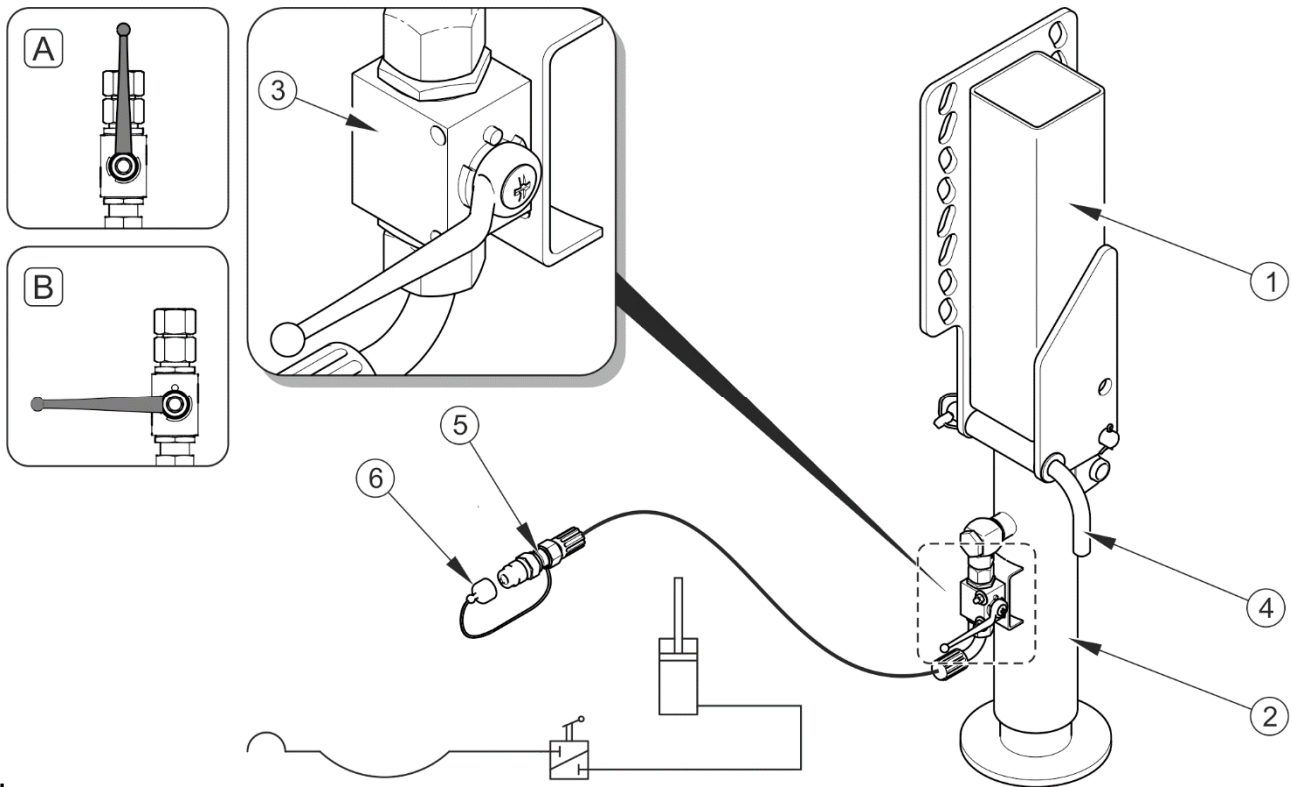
Construction et schéma de l'installation hydraulique de la béquille pliable
